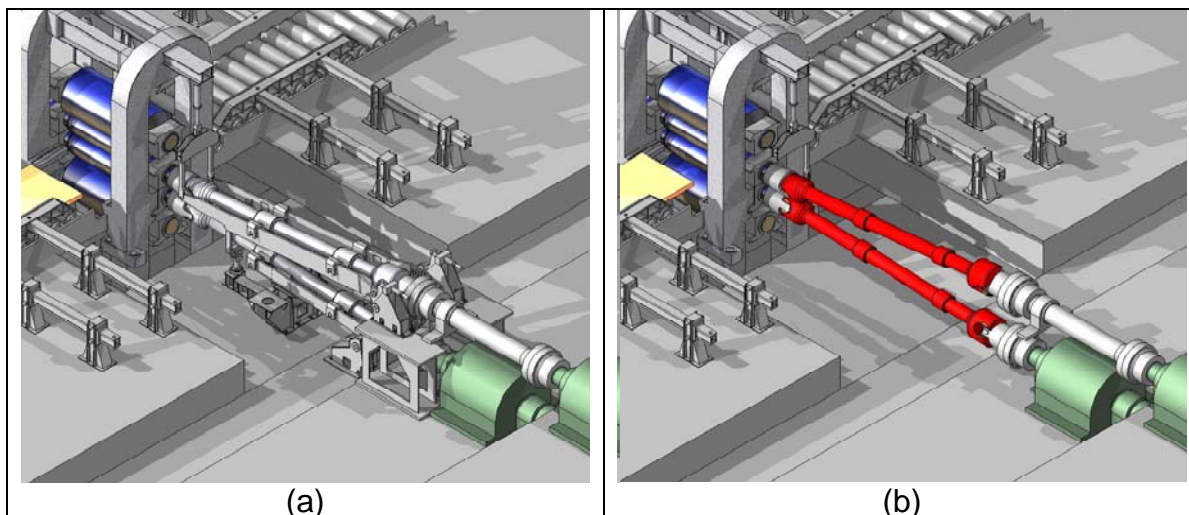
Desenho da montagem do *spindle*: a) montagem completa e b) *spindle* em destaque sem os acessórios.
